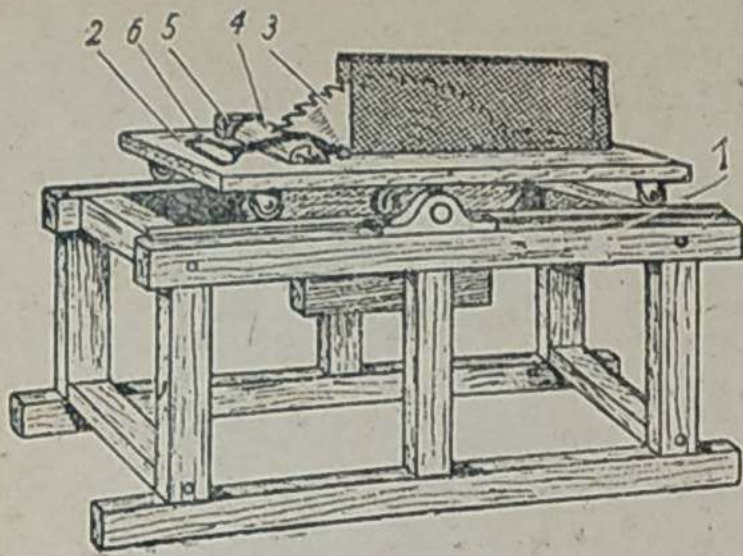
Круглопильный станок с дисковой пилой и неподвижной станиной.
